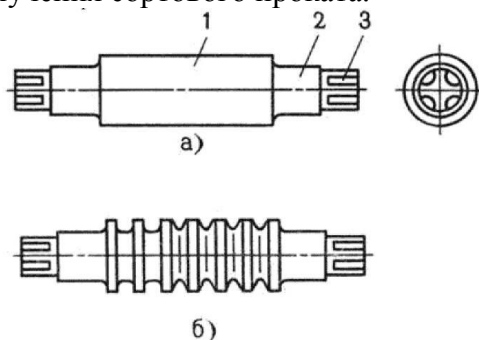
Прокатные валки: а – гладкий; б – калиброванный
